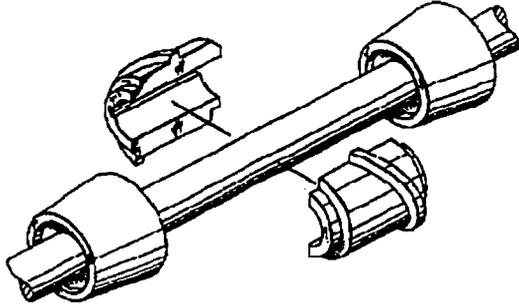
Anillos removibles que forman el tornillo de alta presión [44].
